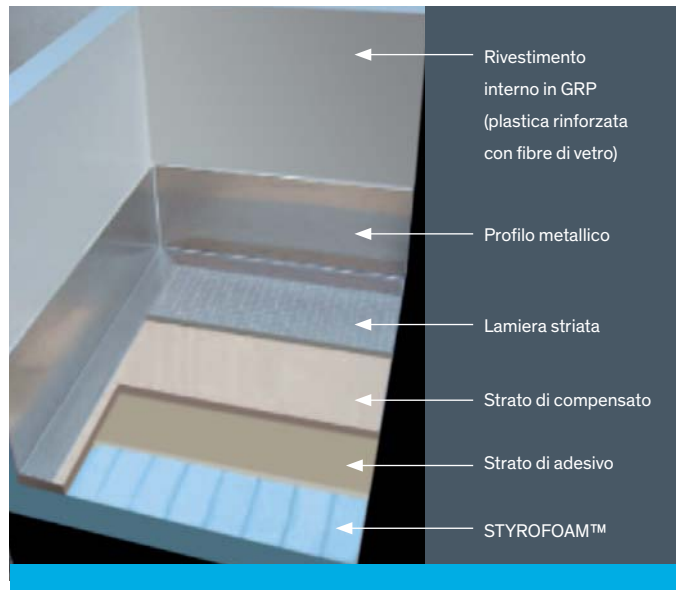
Sezione trasversale di una parete laterale/un pavimento
